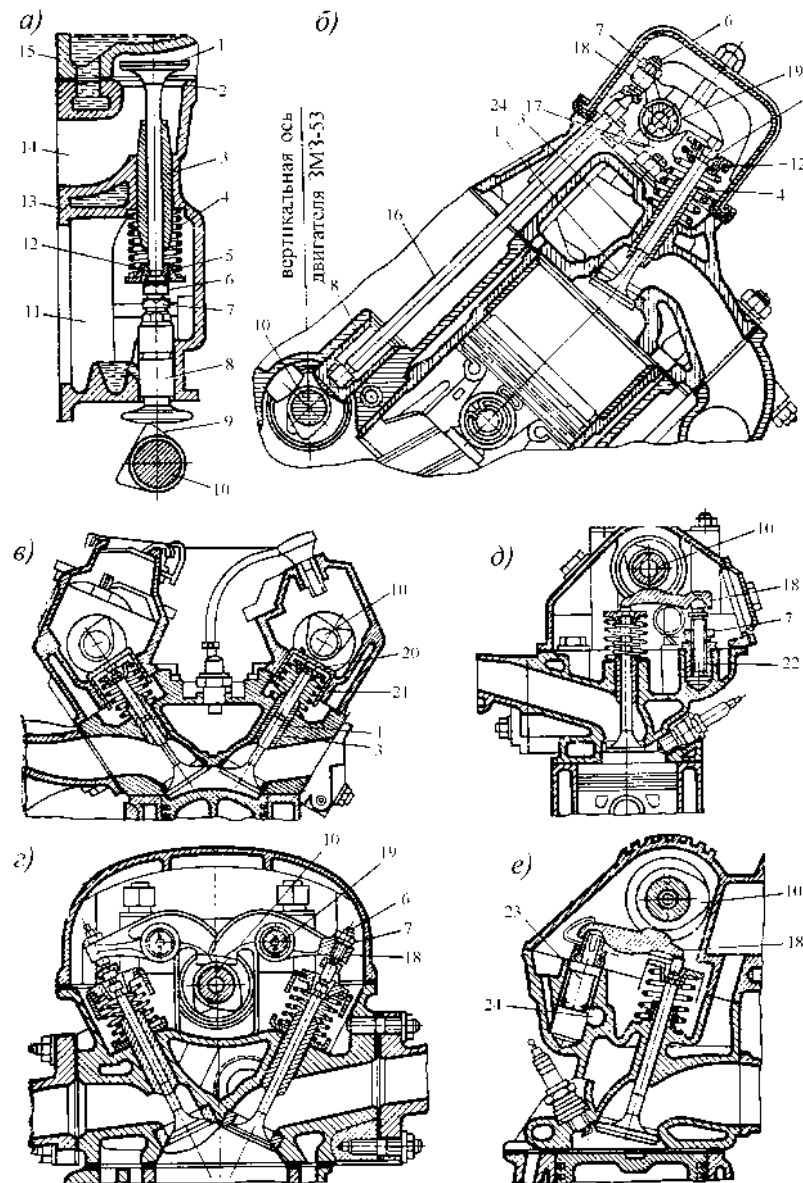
Клапанні механізми газорозподілу: а) з нижнім розташуванням клапанів; б) з верхнім розташуванням клапанів; в) з направляючим стаканом; г) передача через коромисла; д) з механічною опорою у проміжного важеля; е) з гідравлічною опорою у проміжного важеля
